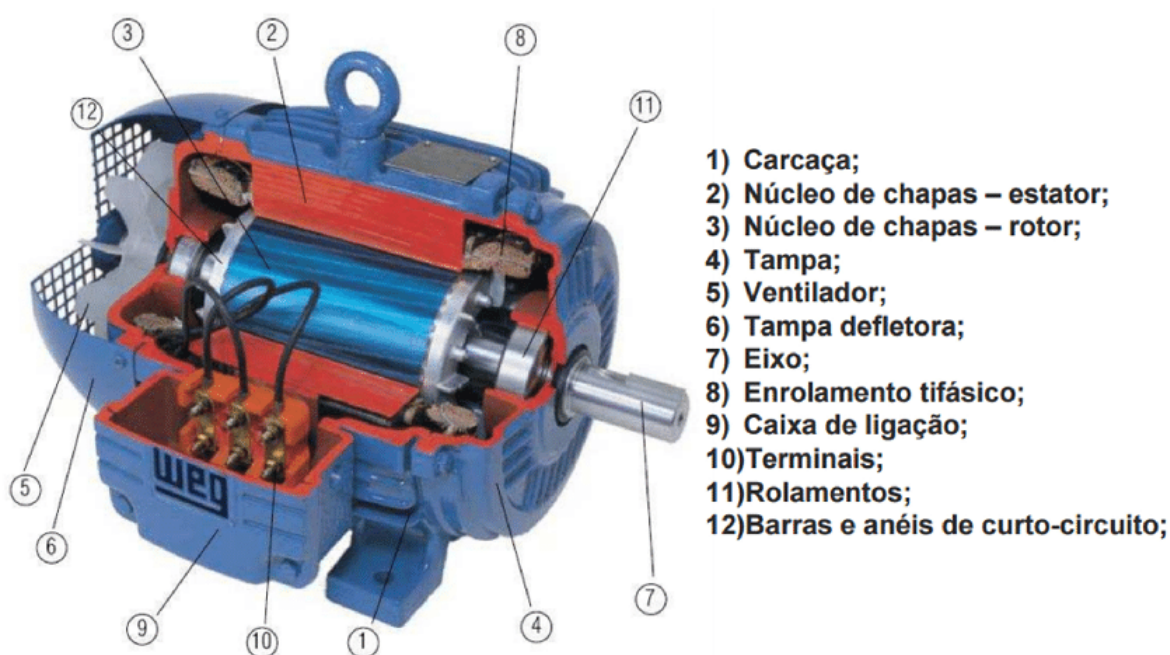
Destaque dos componentes do motor de indução trifásico em uma vista em corte.
